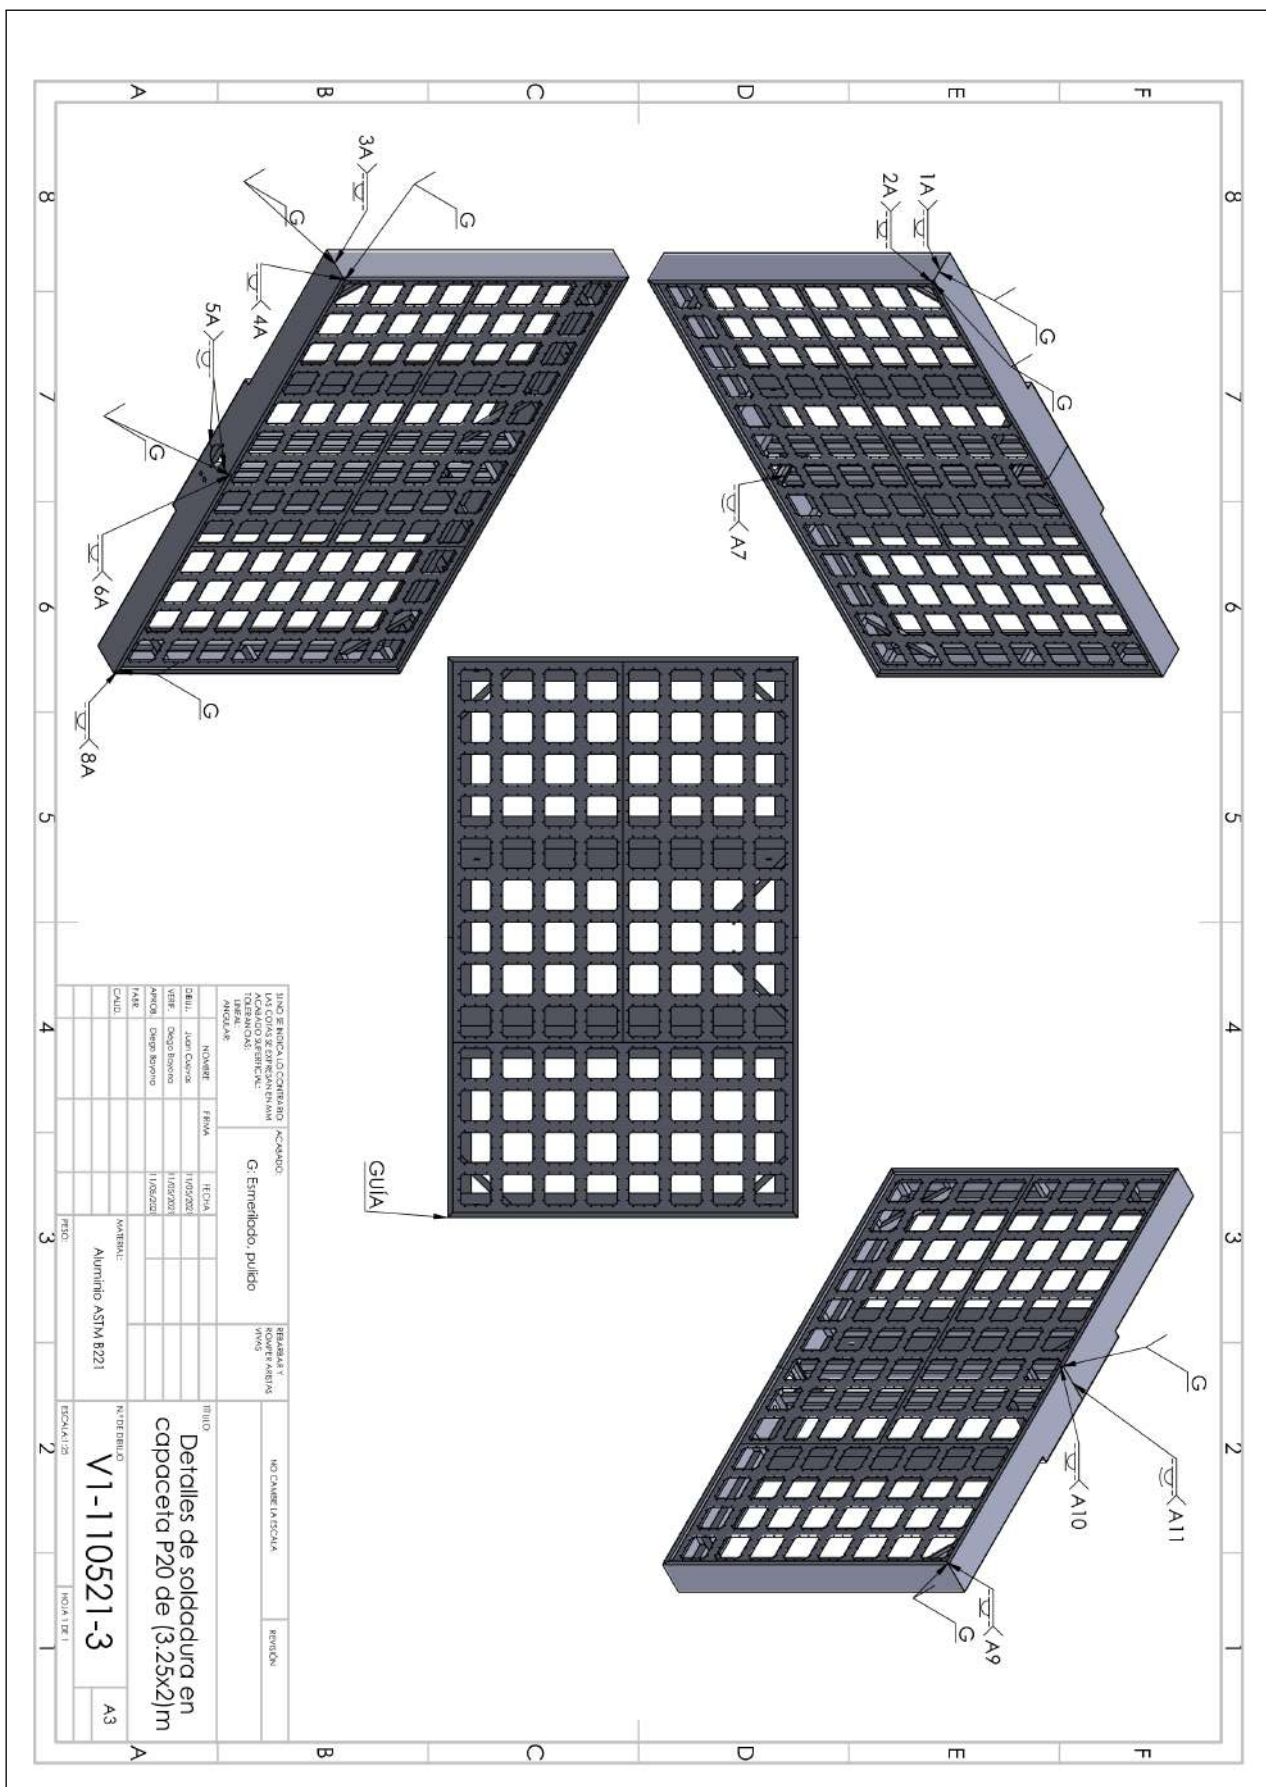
Detalles de soldadura en capaceta P20 uniones A.
